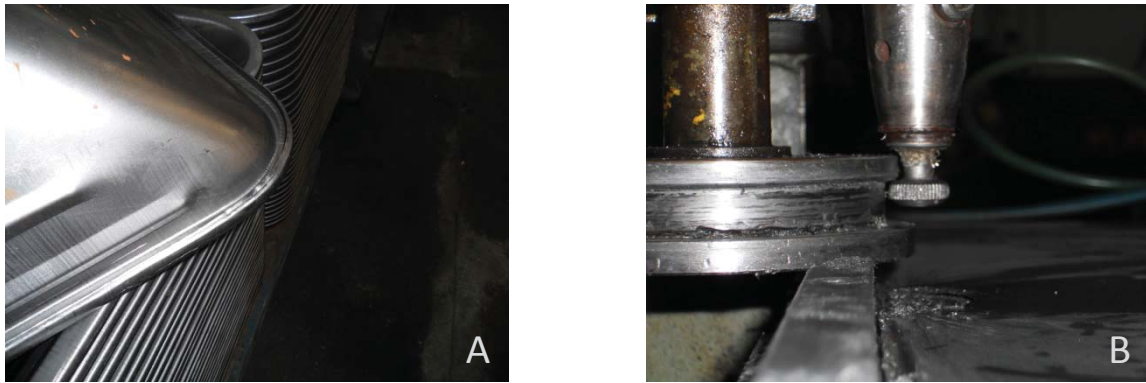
(a) Maceira rebordada. (b) Pormenor da máquina de rebordear.
